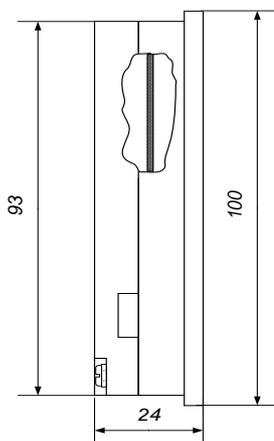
Габаритный чертеж ПЛК серии MC. Вид сбоку.
